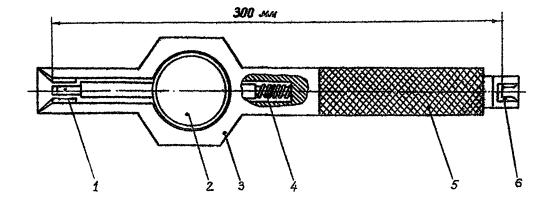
Съемно-индикаторний прибор конструкции ЦНИИС: I - подвижной нож; 2 - индикатор часового типа; 3 - корпус; 4 - пружина; 5 - ручка; 6 - неподвижный нож
